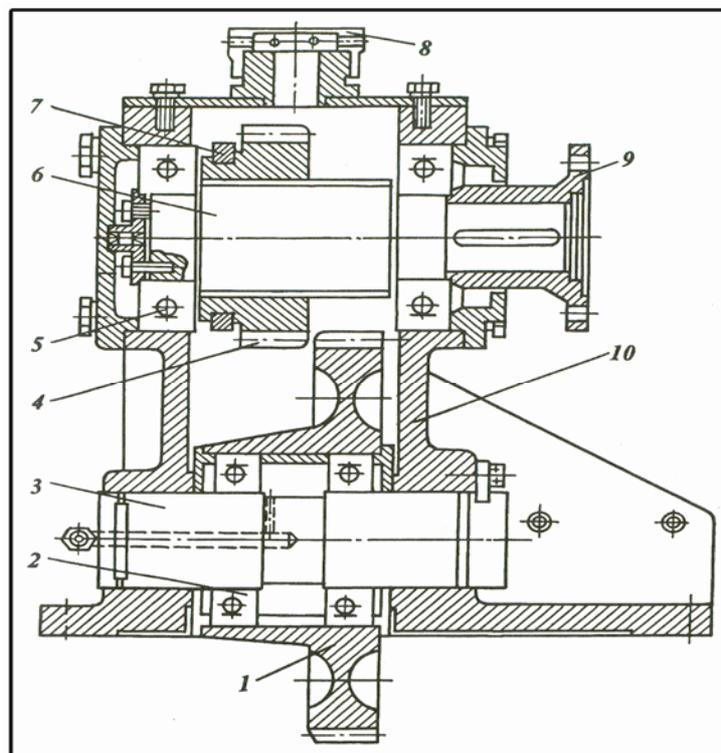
коробка отбора мощности для привода компрессора установки УС5-30:
